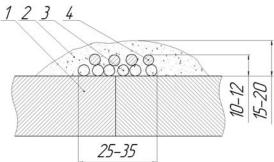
Присадок ППБрХТ 22-2. 1) Основной металл БрХ08; 2) смесь флюсов АН-26 и АФ-4А; 3) Проволока ППБрХТ22-2; 4) Проволока М1
